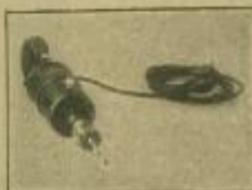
Hand-Bohrmaschine mit bügelförmigem Handgriff und Ausschalter
